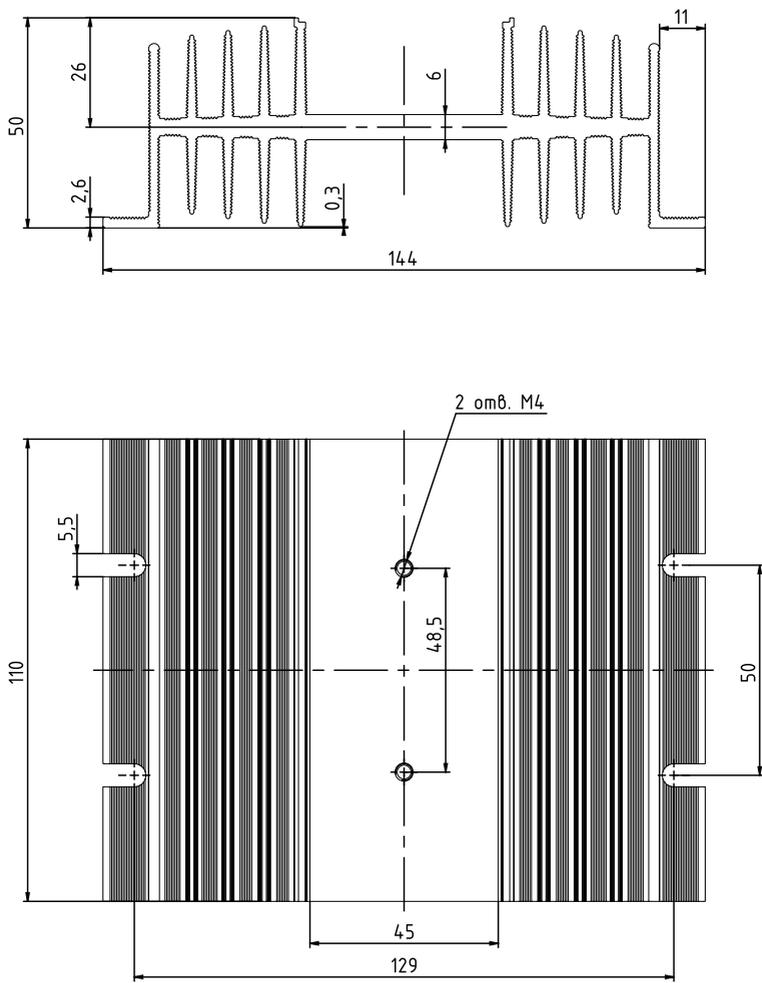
Габаритные размеры радиатора РТР062.1
